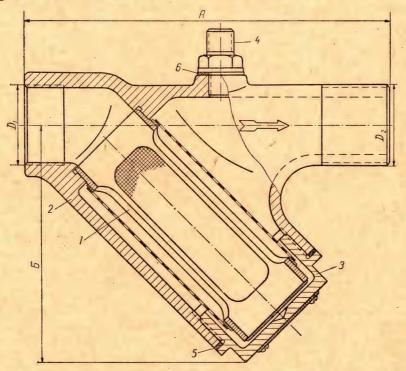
Фильтр угловой сетчатый: 1 — фильтрующая обойма; 2 — корпус; 3 — крышка; 4 — штуцер 3/8"; 5 и 6 — прокладки из паронита.
